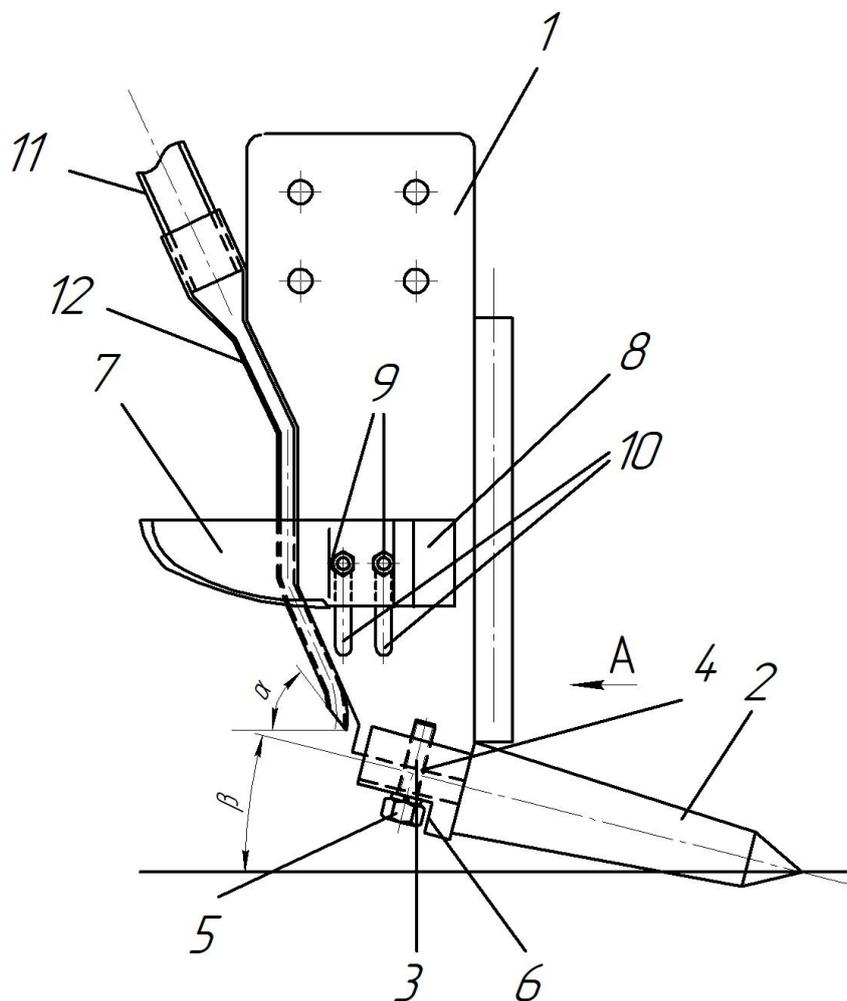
Новый рабочий орган глубокорыхлителя для технологии «strip-till»: 1 – стойка; 2 – долото; 3 – болт; 4 – отверстие в долоте; 5 – головка болта; 6 – рабочая поверхность долота; 7 – подрезающий нож; 8 – хвостовик; 9 – шпильки; 10 – регулировочные пазы; 11 – тукопровод; 12 – анкерная трубка;
